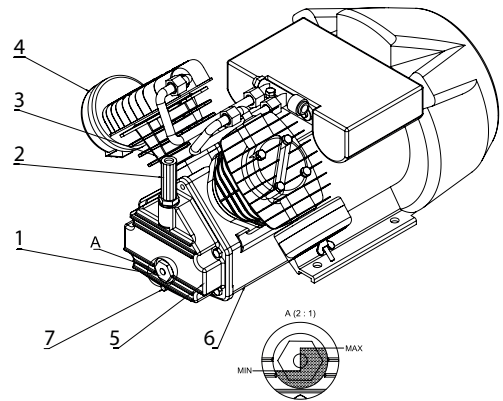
Устройство внешних узлов поршневого блока компрессоров BCD-50-400, BCD-100-400
